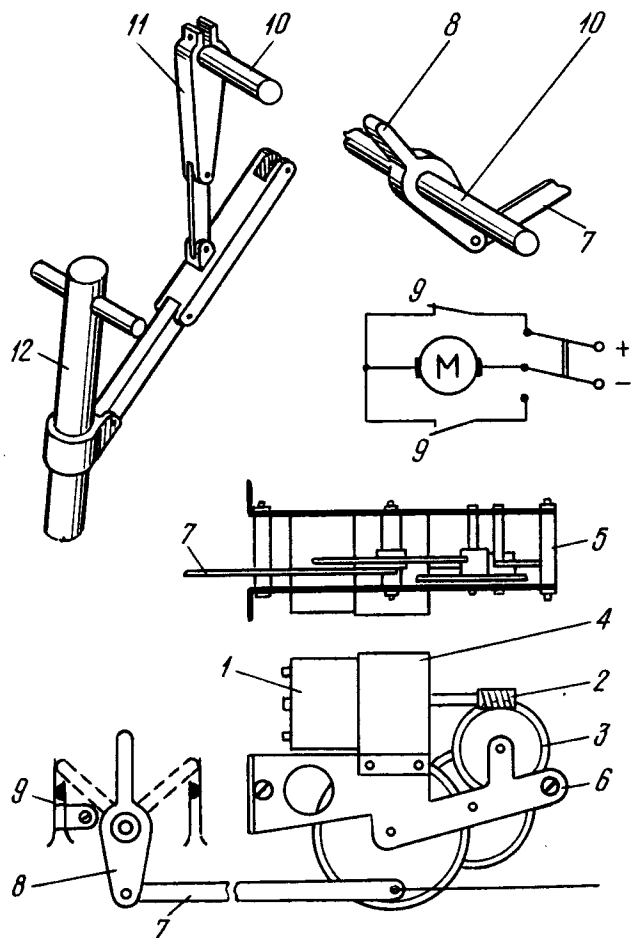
Механизм уборки и выпуска шасси с общей осью:
